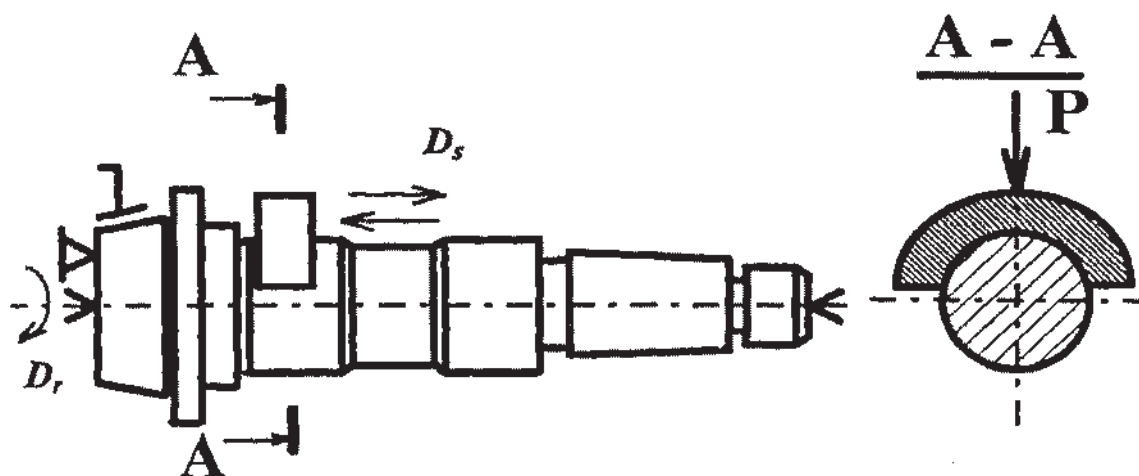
Схема доводки наружной цилиндрической поверхности
